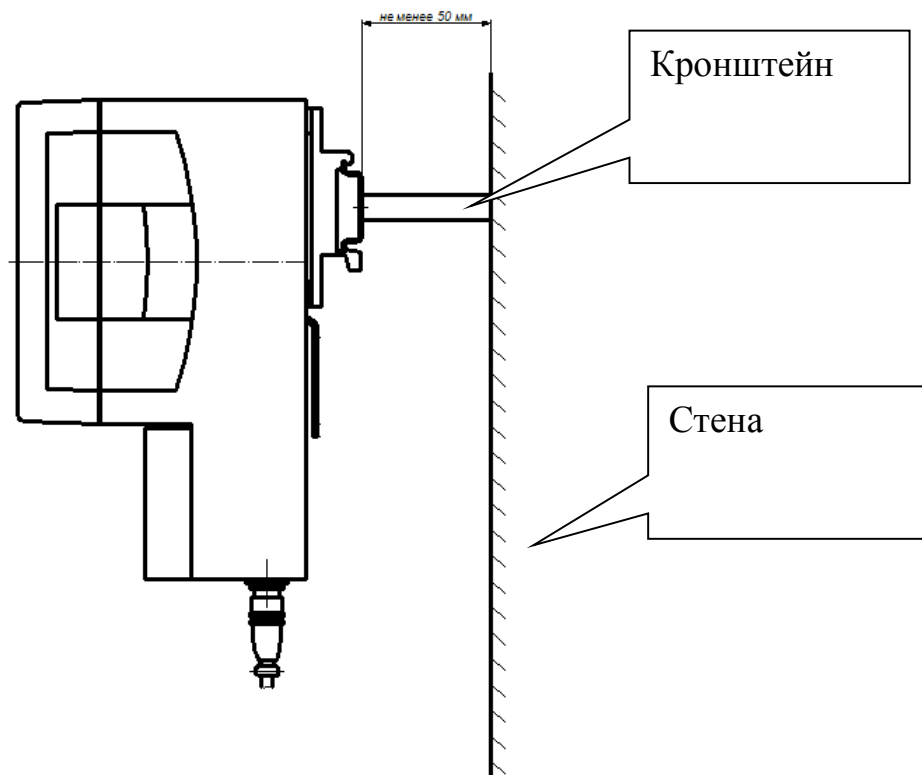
Схема установки корпуса газоанализатора на стену
